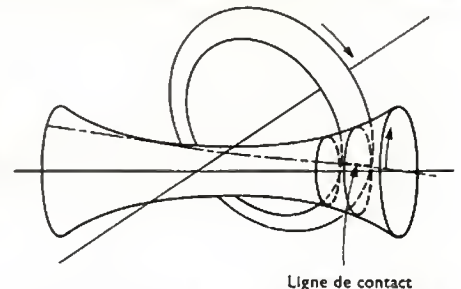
Surfaces primitives d'un engrenage hypoïde
